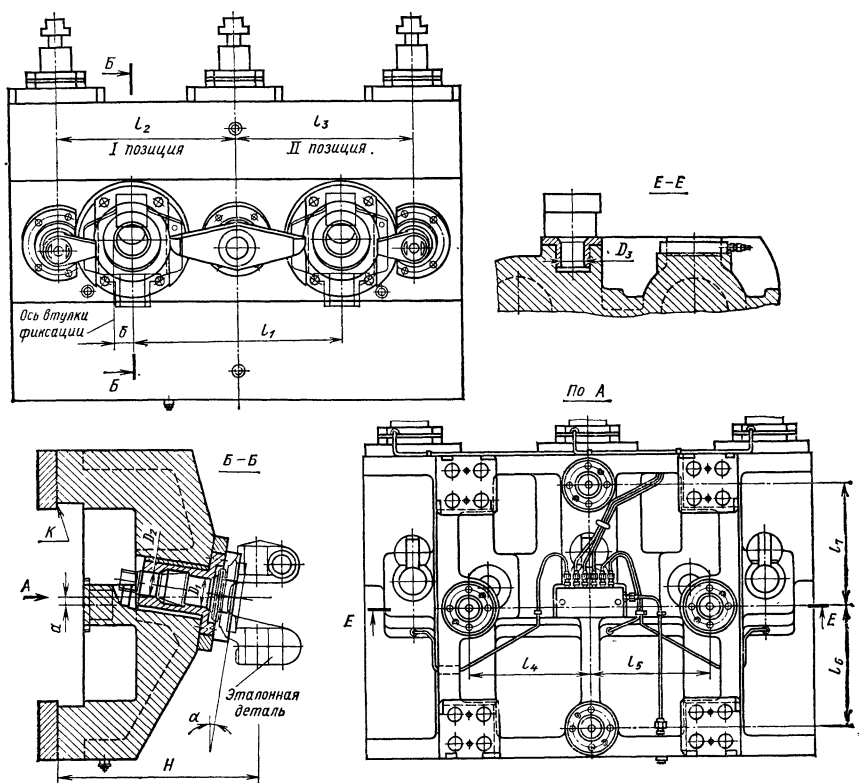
Приспособление-спутник для обработки поворотного кулака автомобиля
